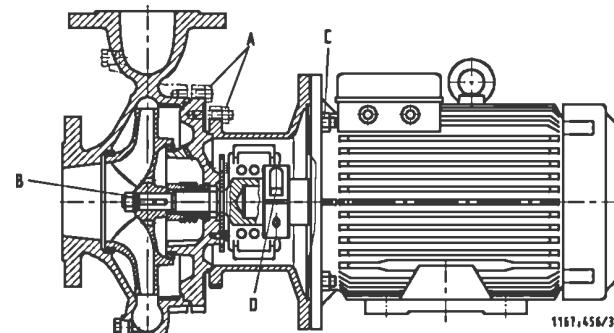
Блочный насосный агрегат с винтовым креплением
